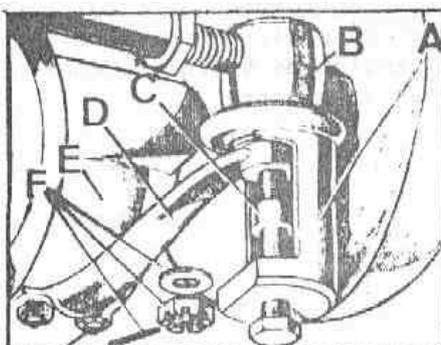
Conexión de la barra de acoplamiento y barra transversal al cárter del pivote de mangueta
